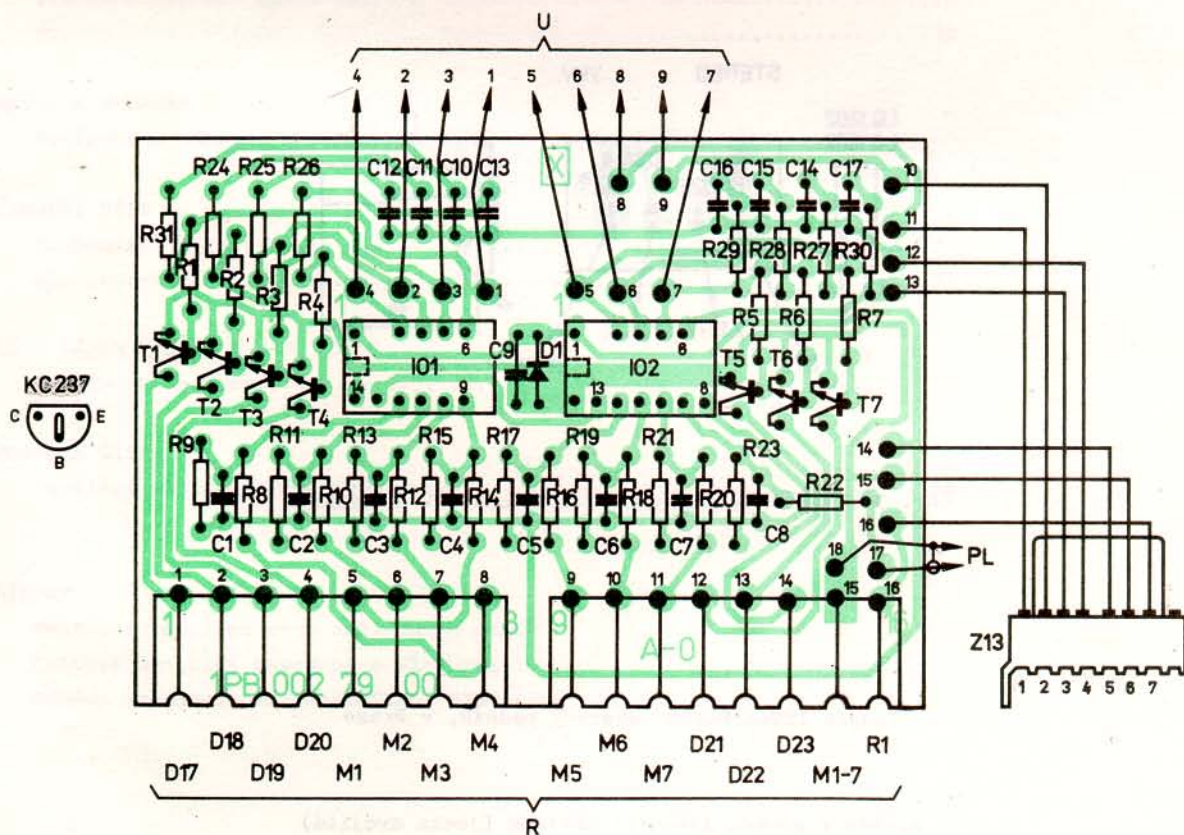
Montážní zapojení indikátoru vyladění pro fm (S2)
